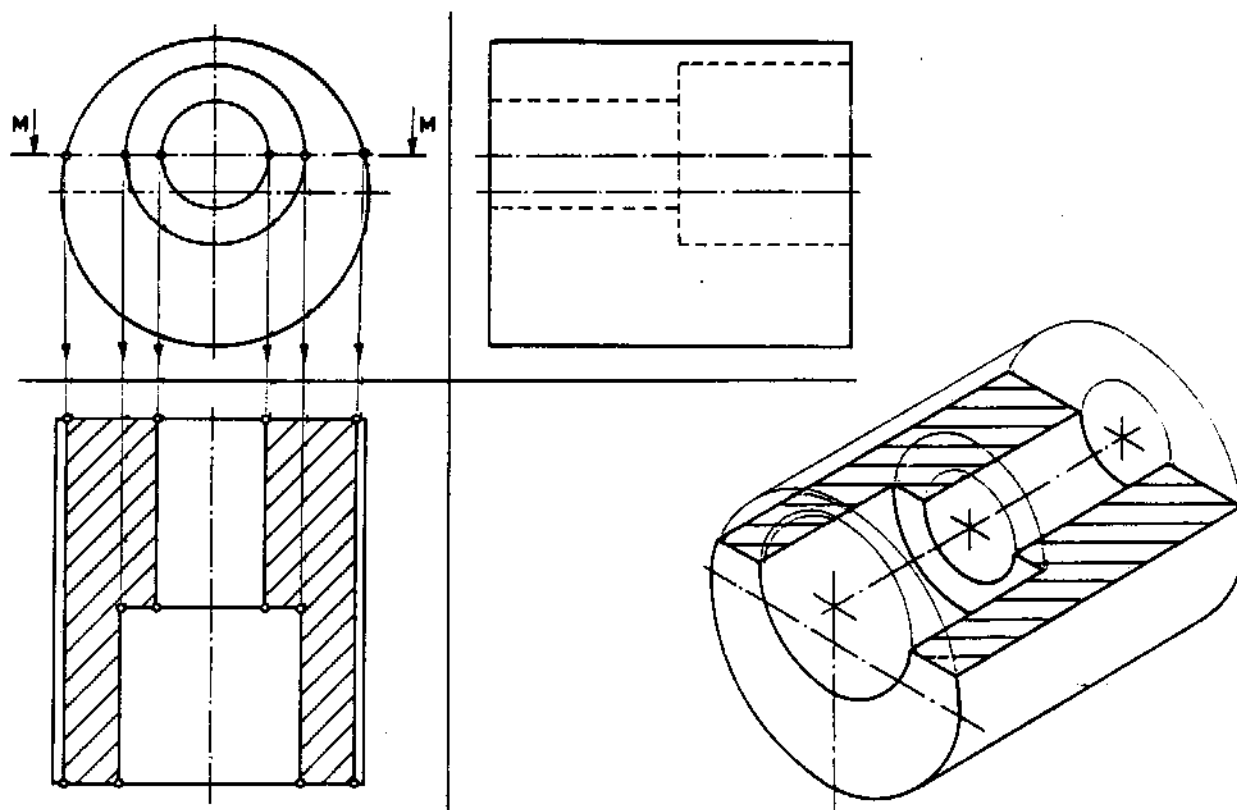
Sezione di un cilindro, con foro eccentrico, mediante un piano di traccia MM passante per l'asse del foro e parallelo al P. O.
